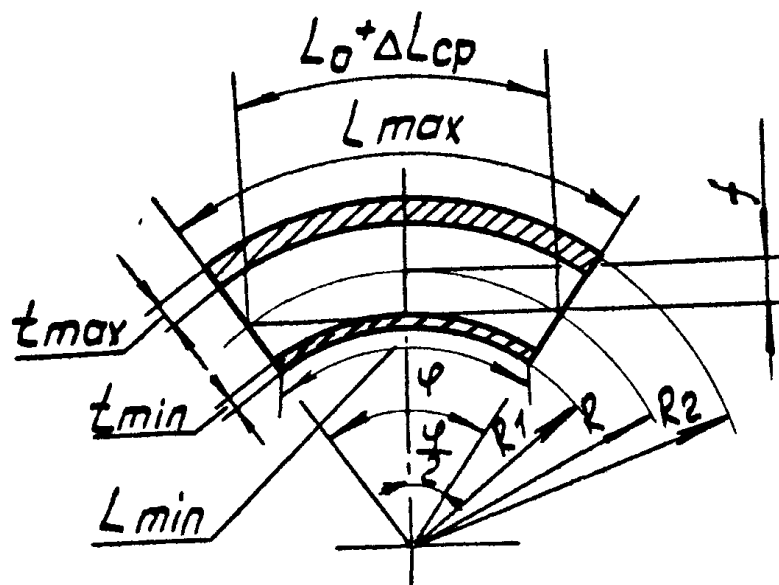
Схема викривлення різнотовщинної заготовки при її роздачі
